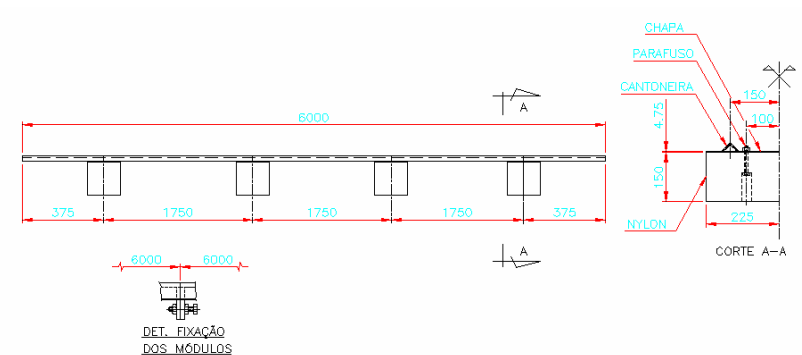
Esquema do módulo e detalhe de fixação.
